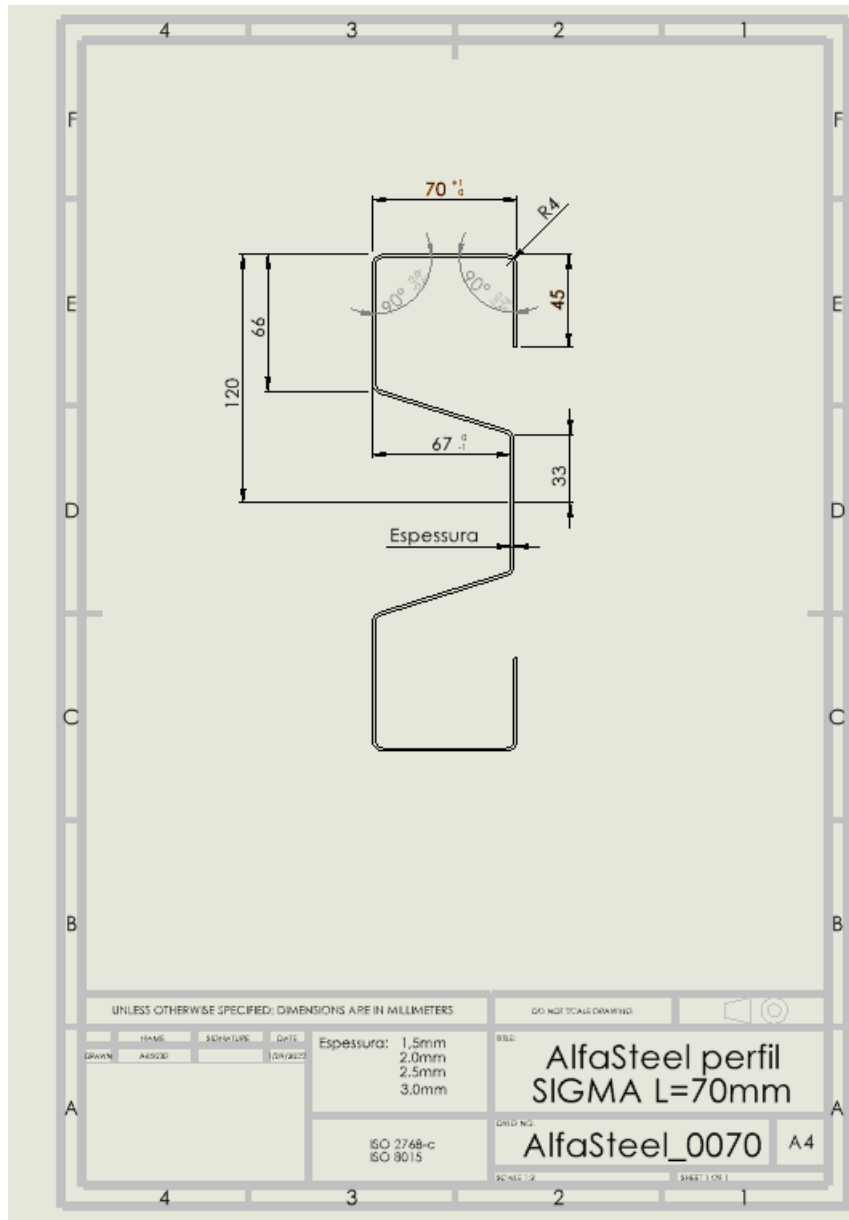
Desenho técnico perfil Largura = 70 mm
